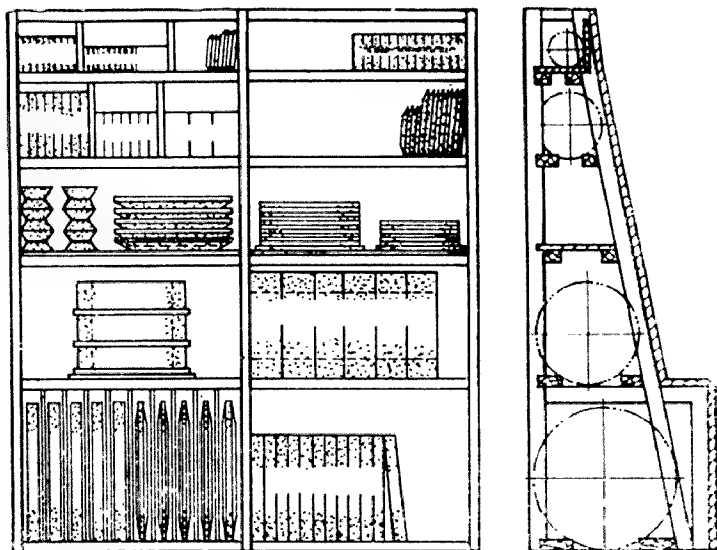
Схема хранения шлифовальных кругов на стеллажах
